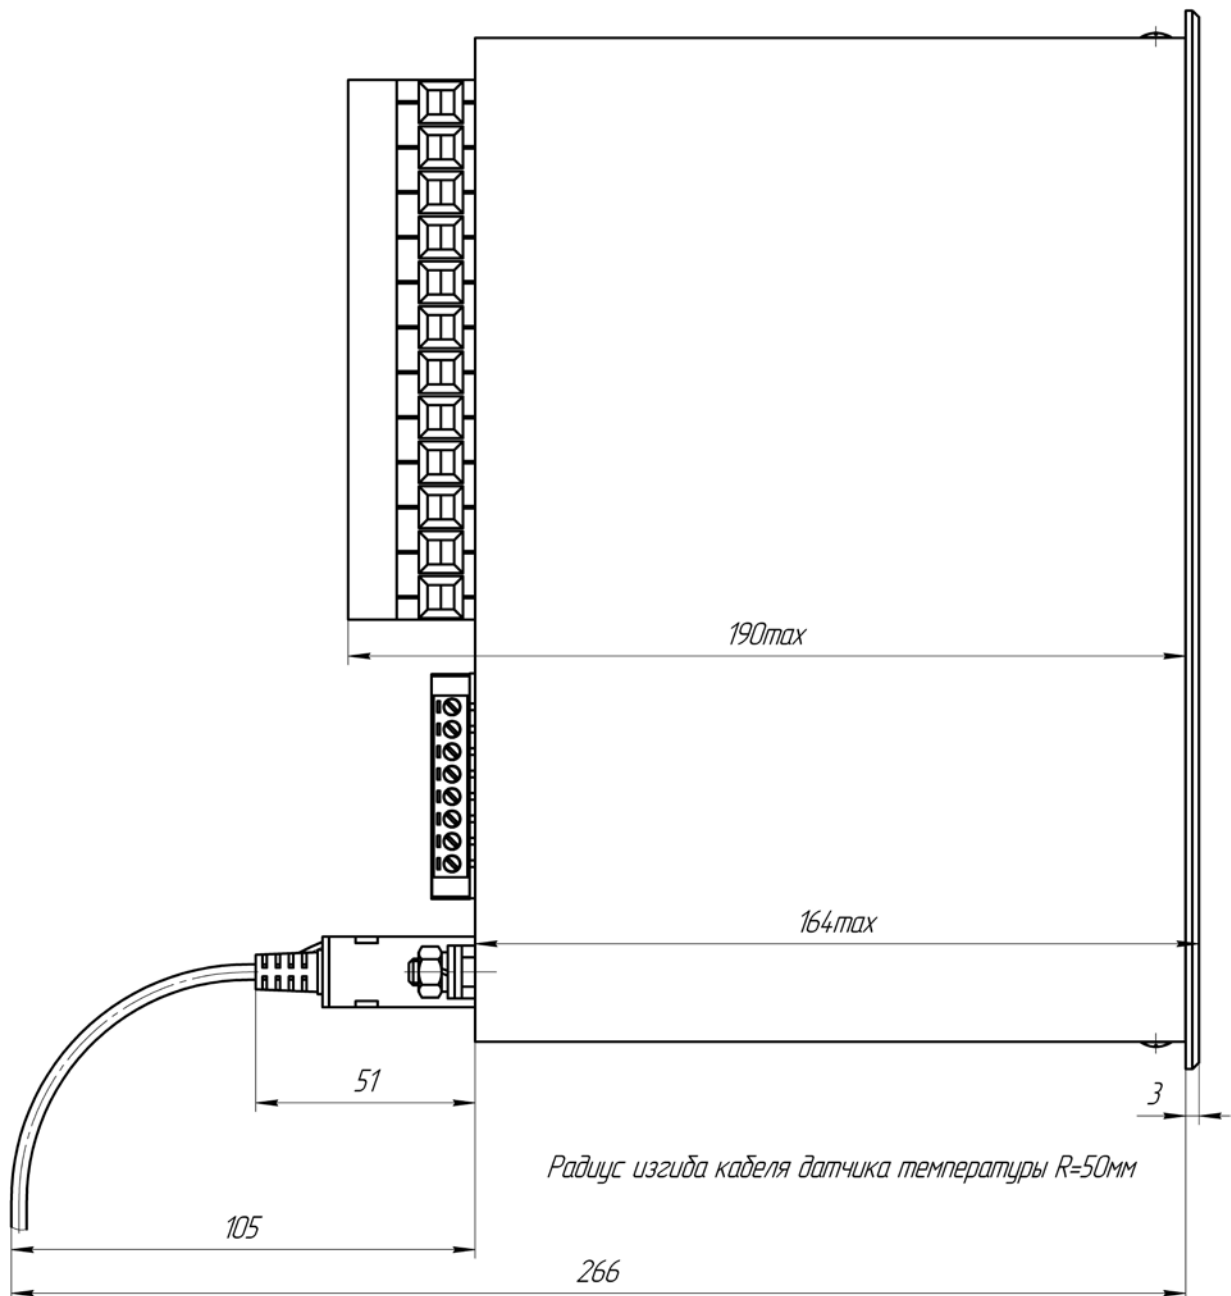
Габаритные размеры устройства РТН-200-05.АХ на виде сбоку
